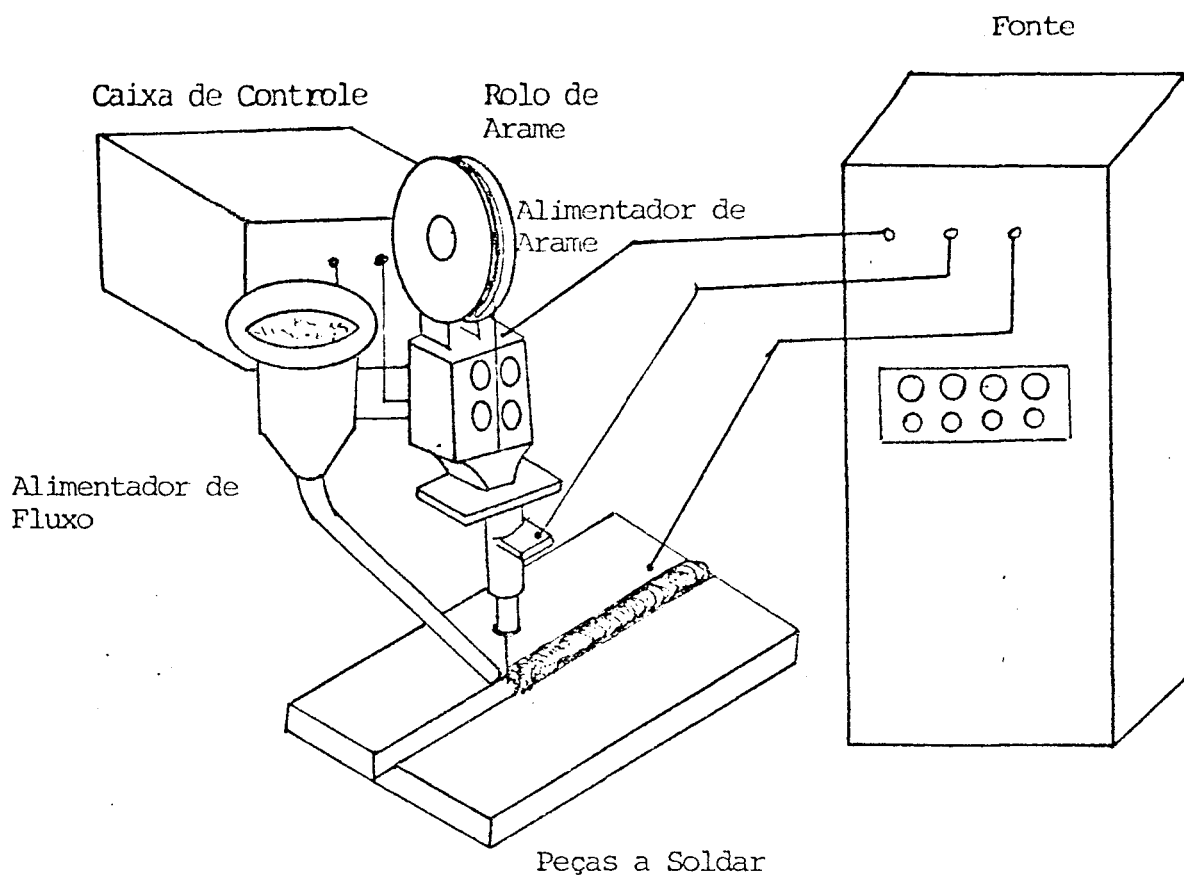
Esquema do Processo de Soldagem a Arco Submerso
